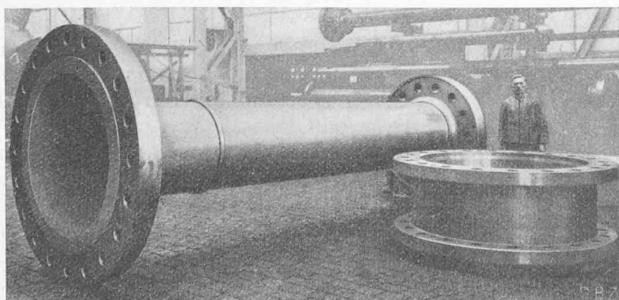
Hohle Turbinenwelle; rechts Laufrad-Servomotorzylinder.
